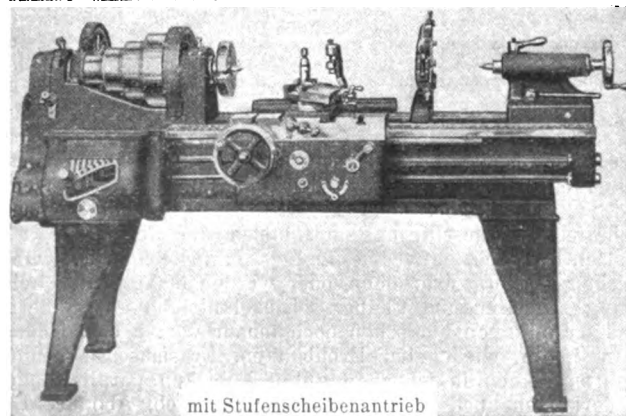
Sondermaschinen für Automobilbearbeitung.
